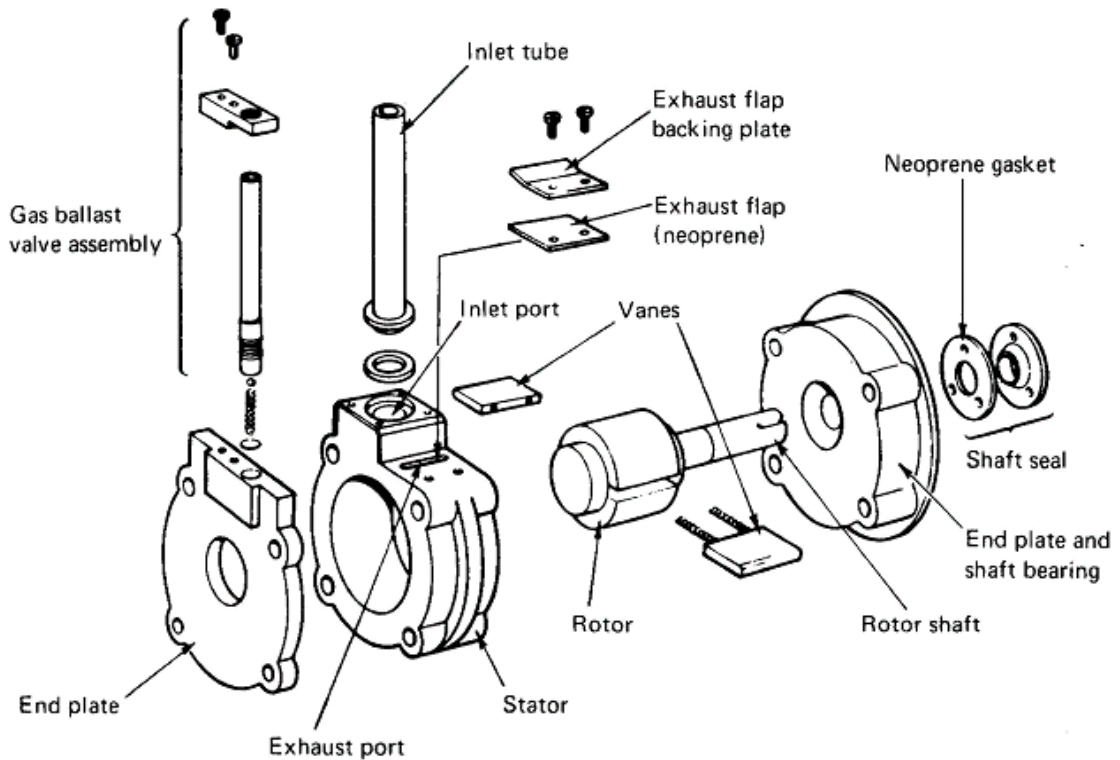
Vista explodida de uma bomba de palhetas rotativas^[27].
